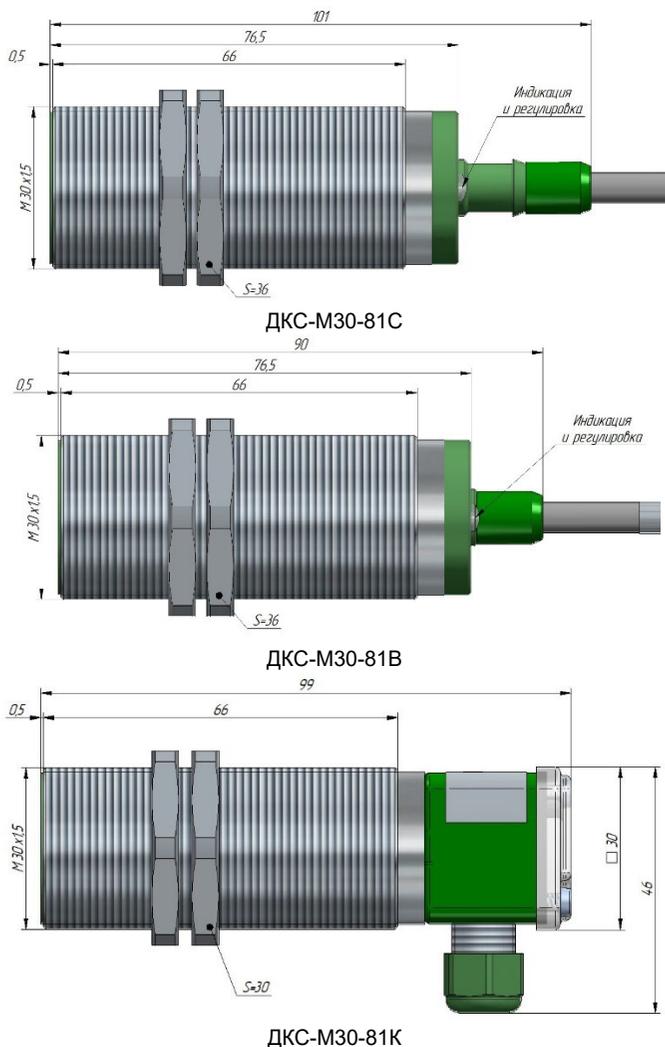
Внешний вид и габаритные размеры датчиков
